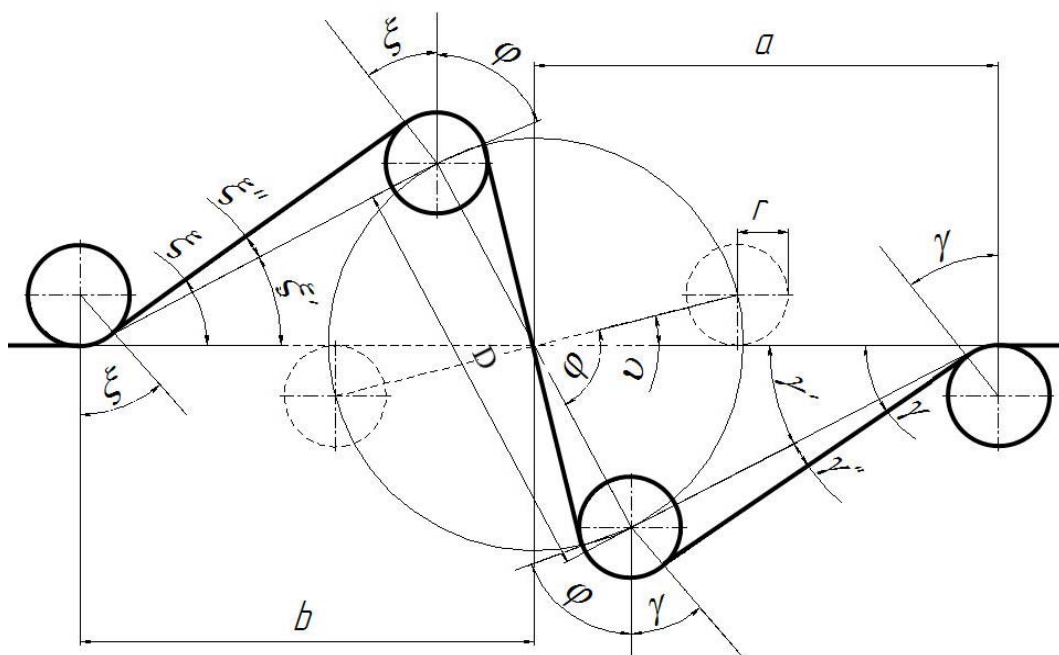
Схема расположения углов охвата нитью основы валов рычажного натяжителя
